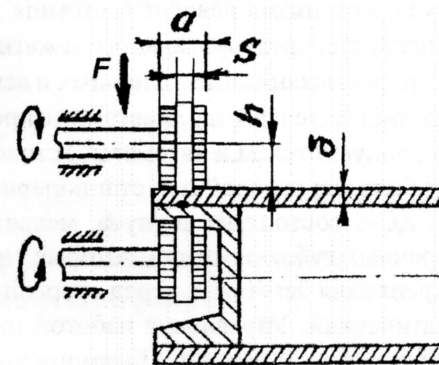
Схема сварки кольцевым замкнутым швом
